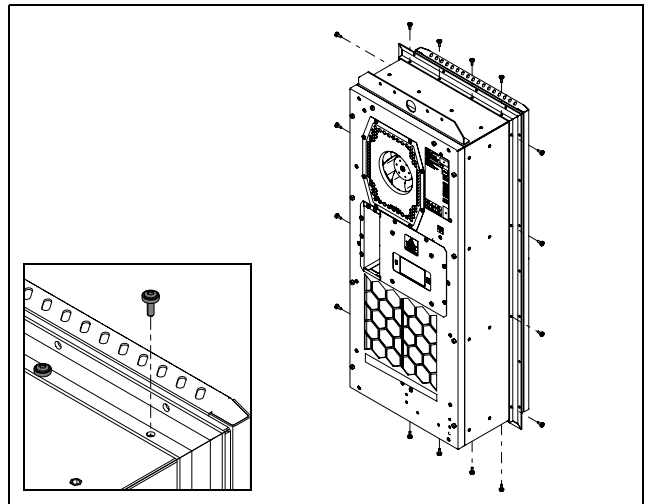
Befestigen des Montagerahmens am Kühlgerät
